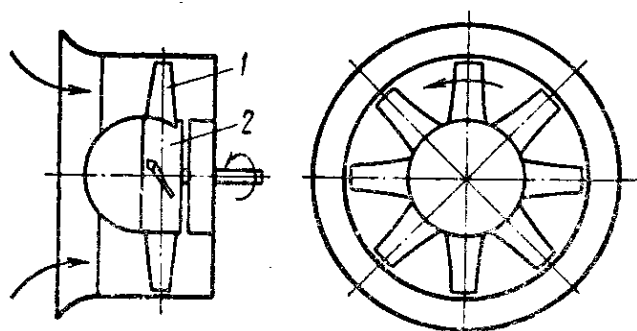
Схема осевого вентилятора: 1 – рабочая лопасть; 2 – втулка рабочего колеса
